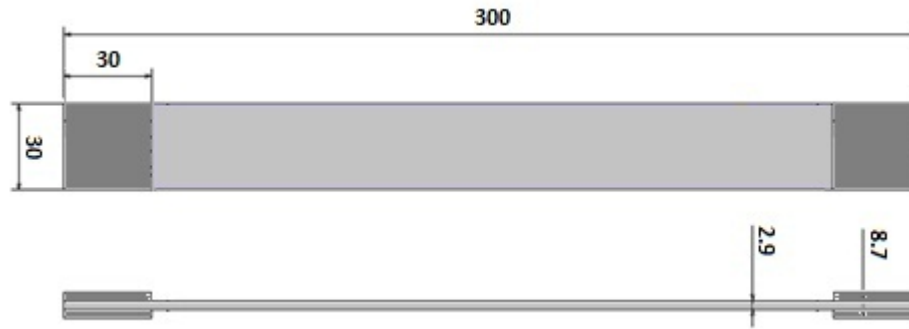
Dimensiones de las probetas de fibra de carbono-aramida/epoxi [mm]
